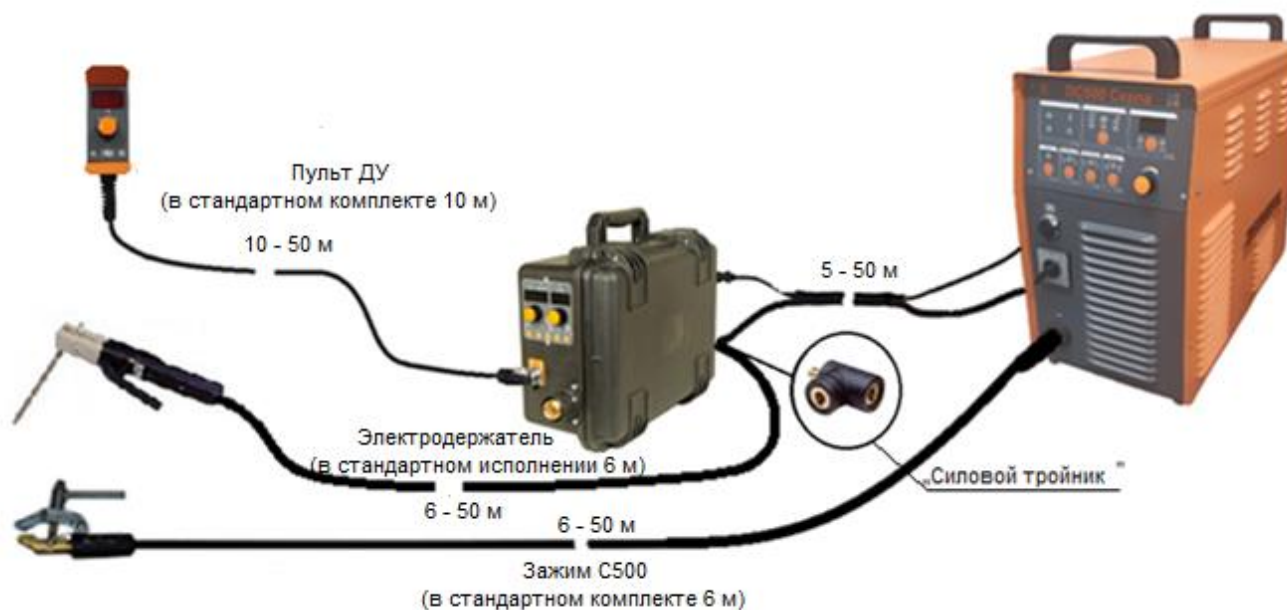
Схема подключения комплекта в режиме сварки РД
